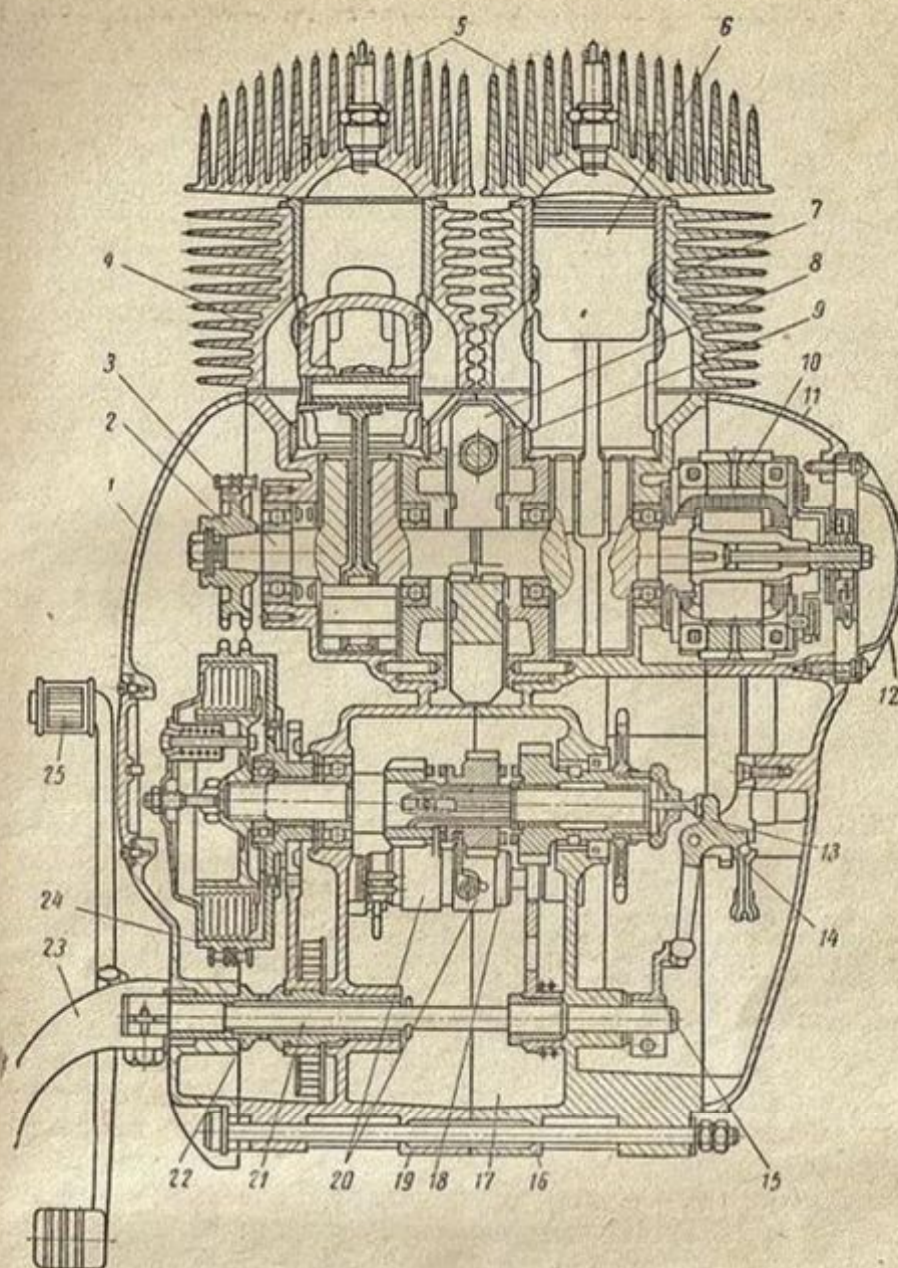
Двухцилиндровый двухтактный двигатель мотоцикла ИЖ «Юни-тер»:
